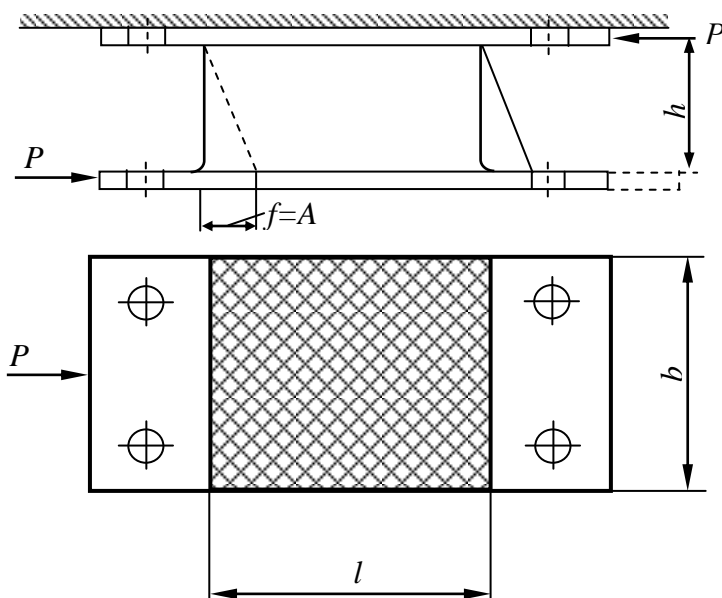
Схема резинометаллического пакета-амортизатора
